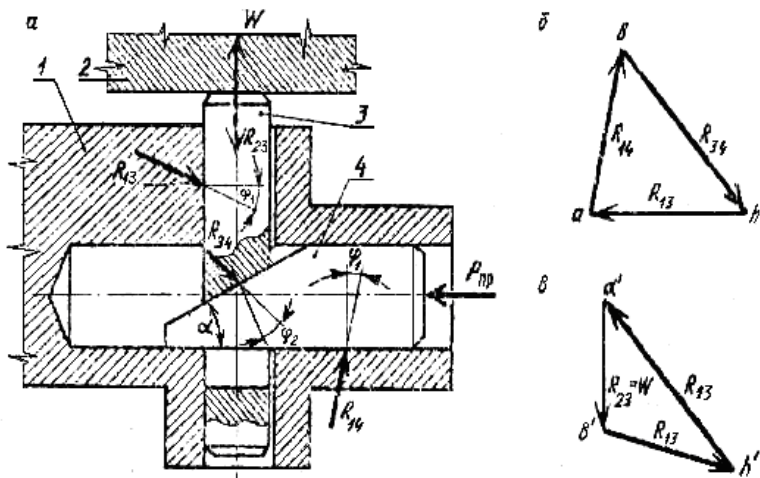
Схема клиноплунжерного механизма: 1 - корпус, 2 - заготовка, 3 -одноопорный плунжер, 4 – односкосный клин
